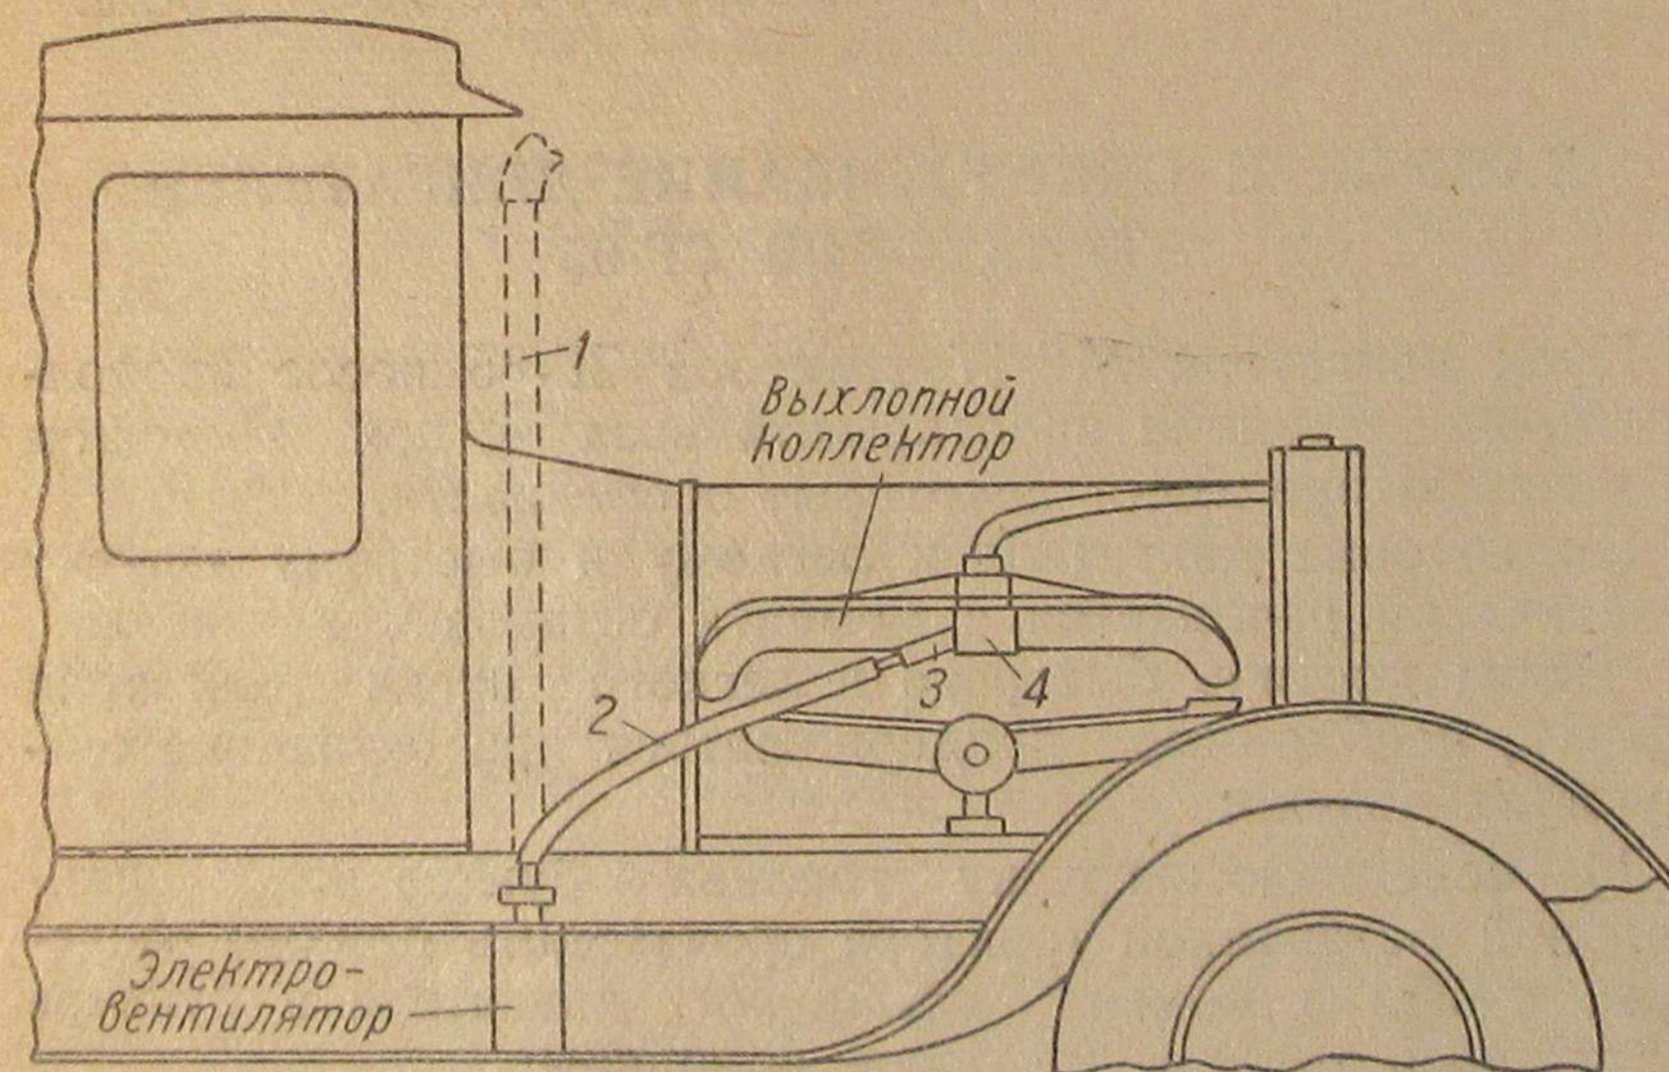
Подогреватель воздуха ЦНИИМЭ
